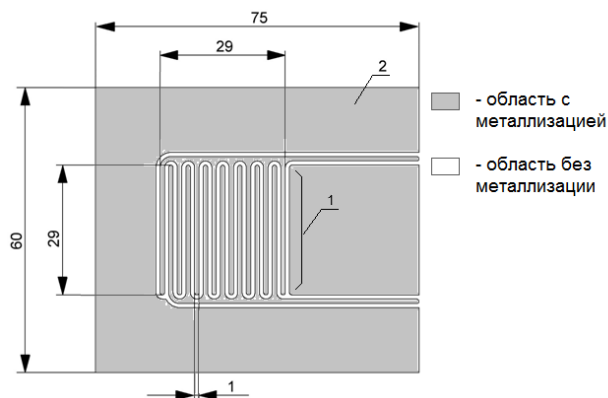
Конструкция накладного измерительного ленточного конденсатора
